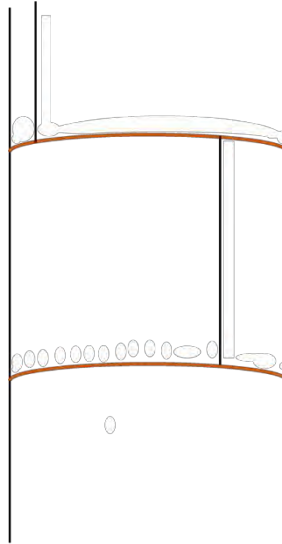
Esquemático de soldadura y remachado de la coraza
